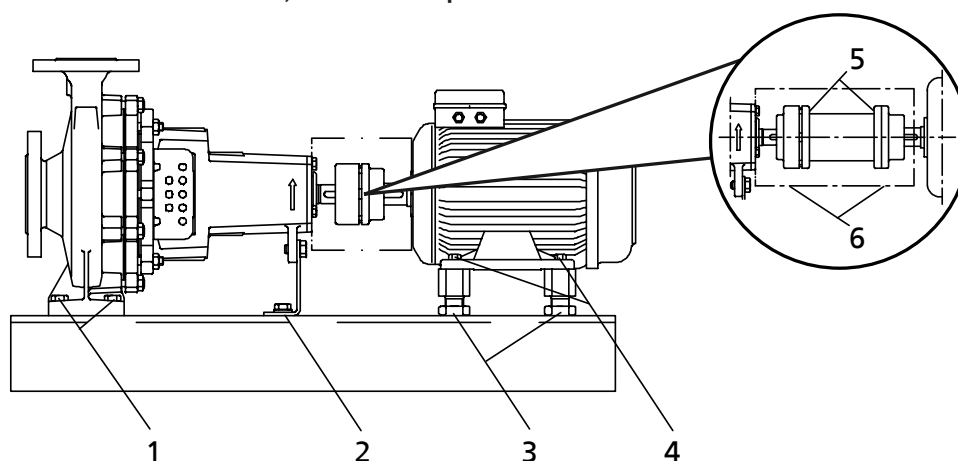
Места затяжки резьбовых соединений насосного агрегата
